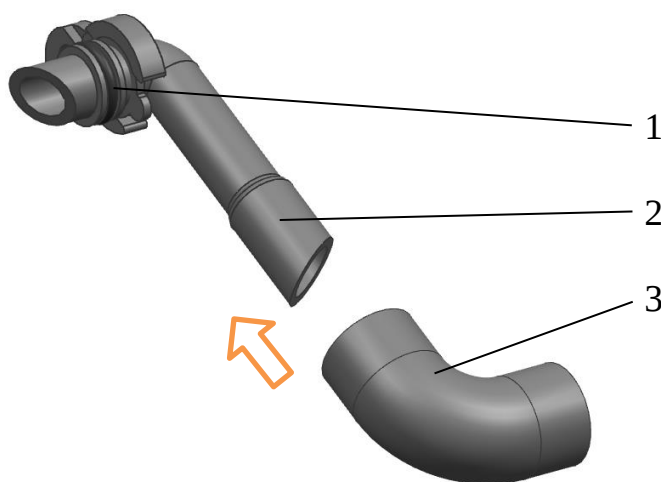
Подсборка трубки вентиляции с угловым шлангом:
